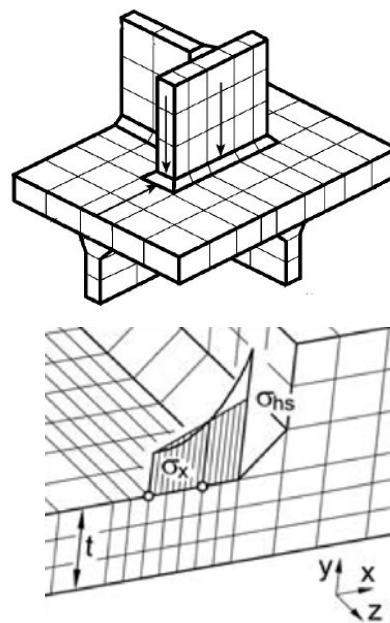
Расчетная схема сварного соединения для определения напряжений в «горячей точке»
